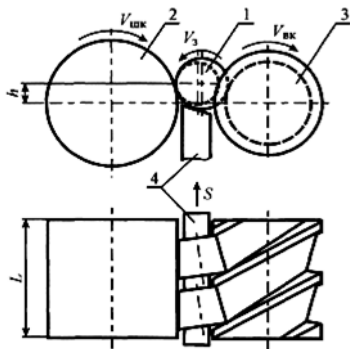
Схема безцентрового шліфування конічних поверхонь
